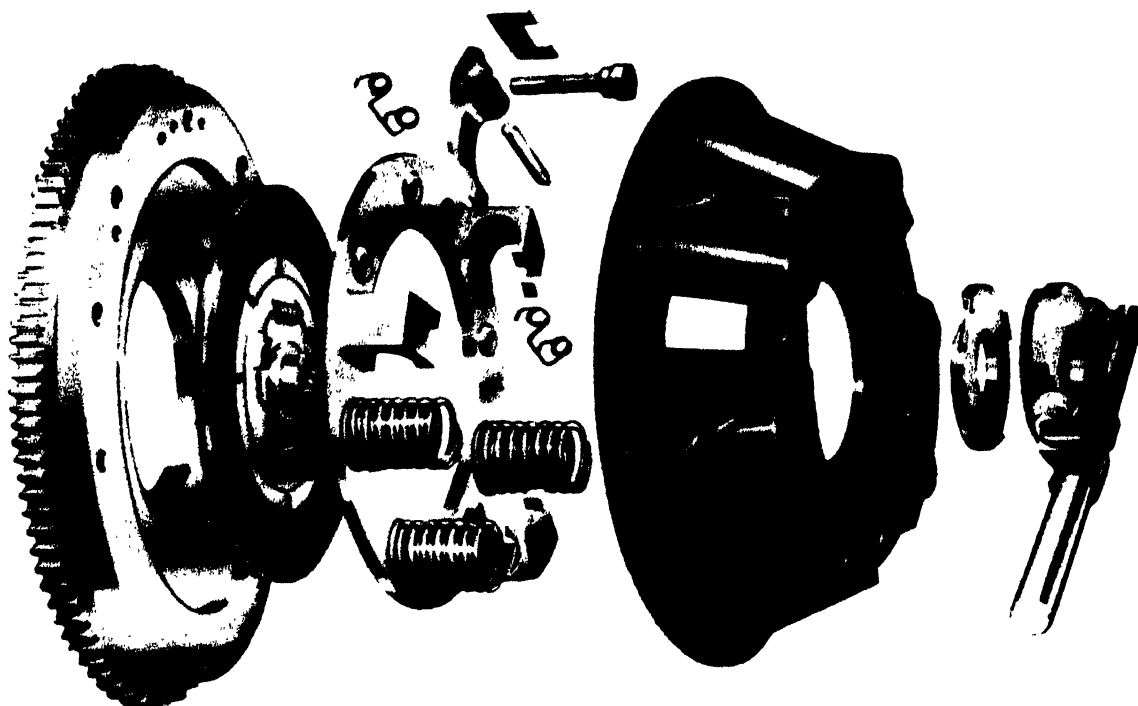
PIECES D'UN EMBRAYAGE A FRICTION DE VEHICULE
